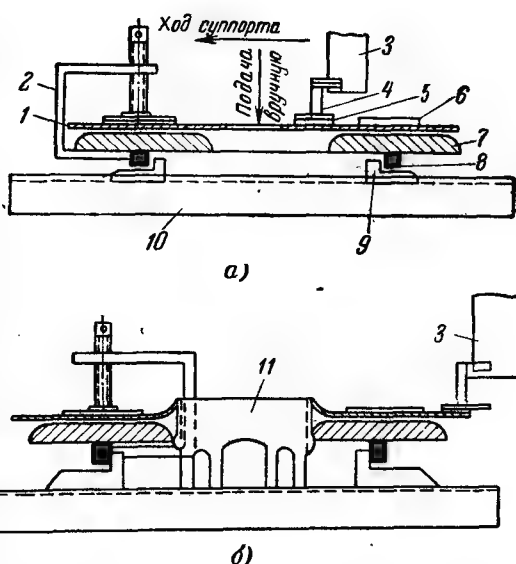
Отбортовка кромок заготовки линзового компенсатора.
